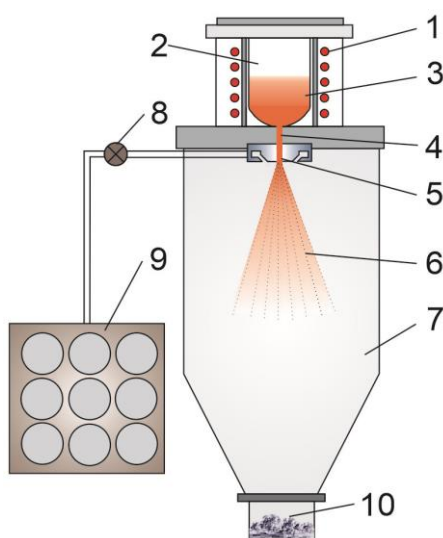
Схема установки для газового распыления: 1 – высокочастотная индукционная печь; 2 – керамический огнеупорный тигель; 3 – расплавленный металл; 4 – металловыпускная трубка; 5 – распылительная форсунка; 6 – распыляемый струей инертного газа металл; 7 – распылительная колонна; 8 – клапан управления давлением газа; 9 – баллоны с распылительным газом; 10 – полученный порошок [206]
